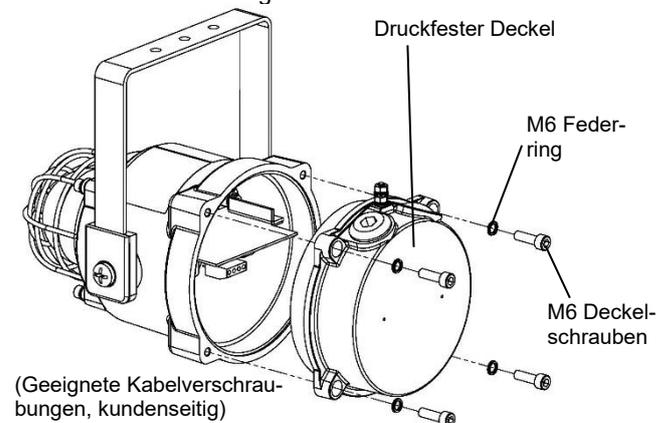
Zugang zum explosionsgeschützten Gehäuse
